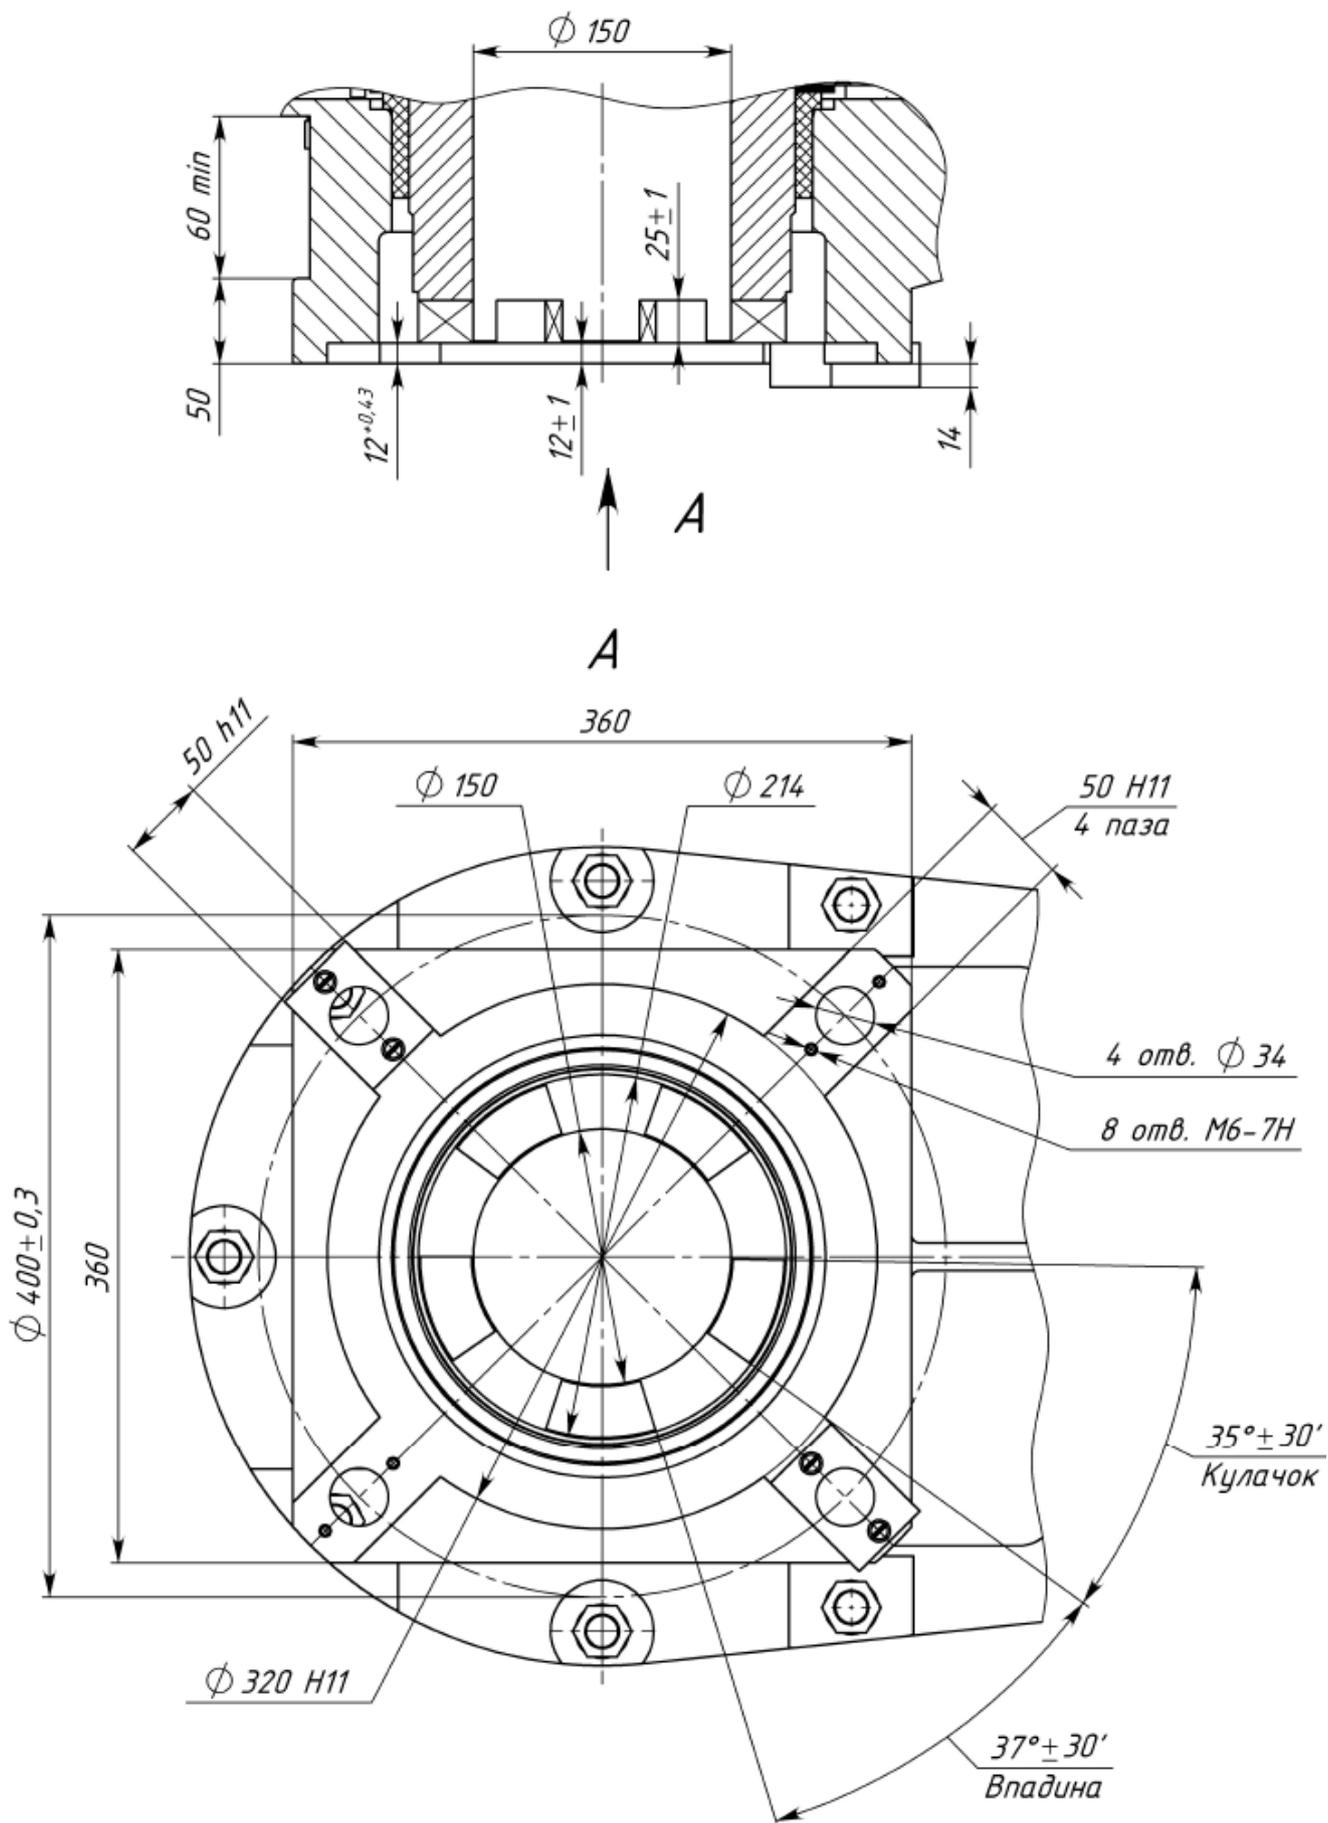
Присоединение типа Д для конструктивной схемы 430
